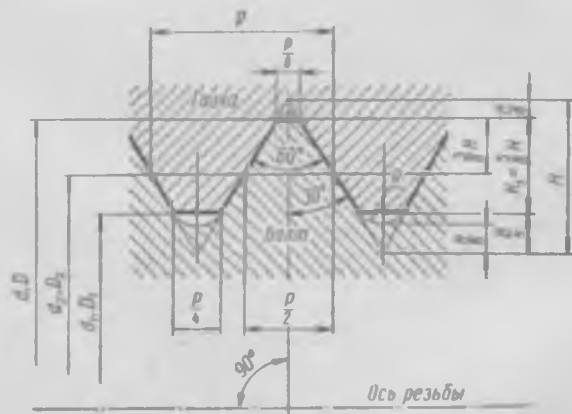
Метрическая резьба по СТ СЭВ 180—75
